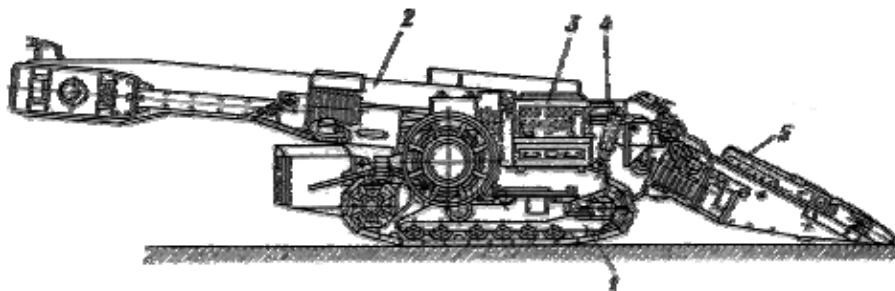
Загальний вигляд і основні вузли вантажної машини ПНБ-4:
